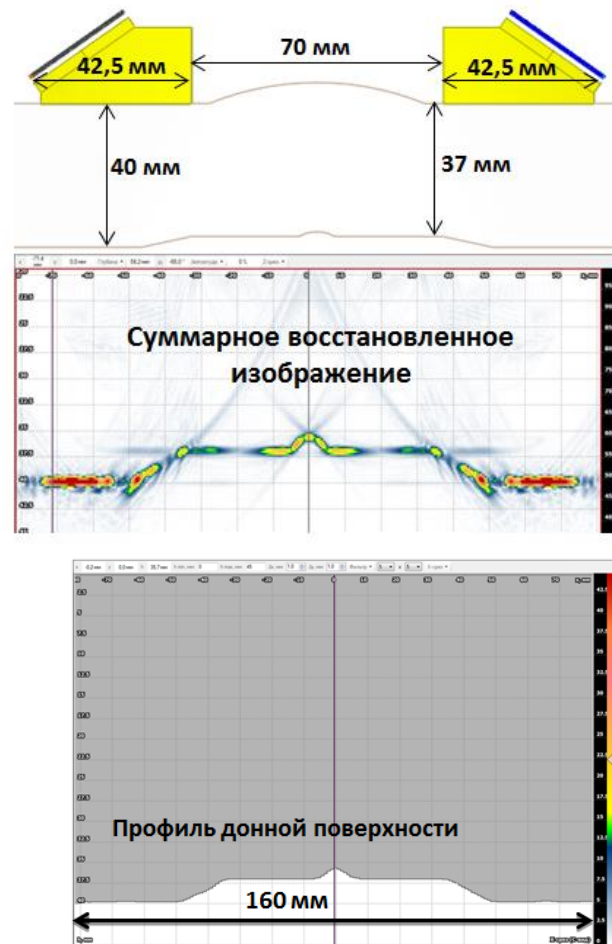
Профиль донной поверхности сварного соединения с вогнутым внутренним валиком
